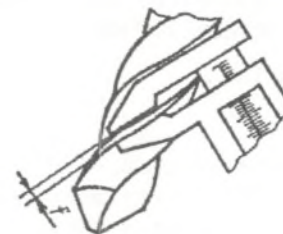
Измерение длины поперечной кромки и ширины ленточки сверла штангенциркулем
